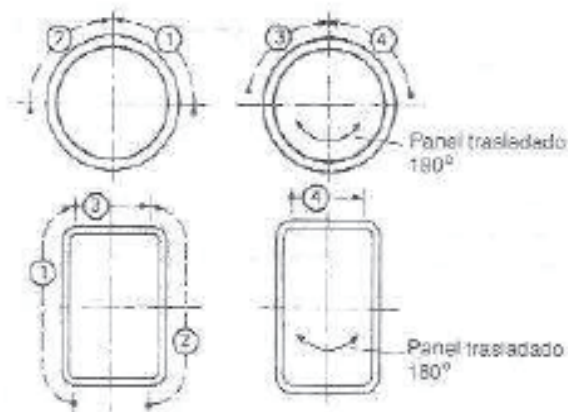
Soldadura vertical ascendente de 180°
